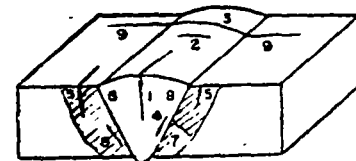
Tipos diversos de grietas en una soldadura a tope.
